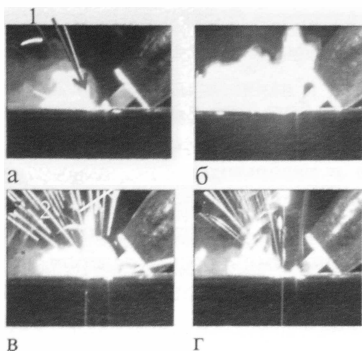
Поведение эрозионного факела при лазерной сварке углеродистой стали: $P = 5$ кВт; $V_{св} = 2$ м/мин. Защита He – 17 л/мин; 1 – приповерхностная плазма; 2 – плазма каверны; а, г – плазма каверны не закрыта; б, в – плазма каверны закрыта
